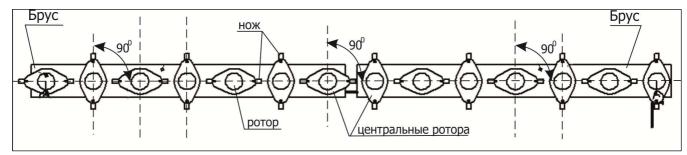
Регулировка роторов режущих аппаратов
